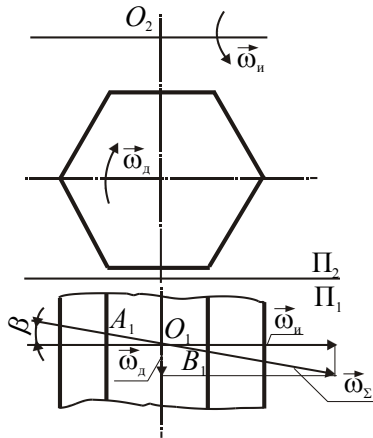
Схема обробки багатогранного вала при взаємноперпендикулярних осях заготовки й інструмента
